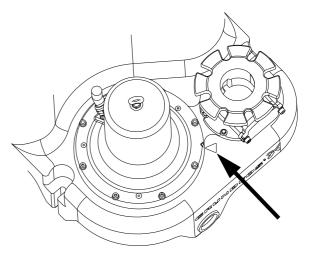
Метки совмещения на резервуаре и фланце насоса
